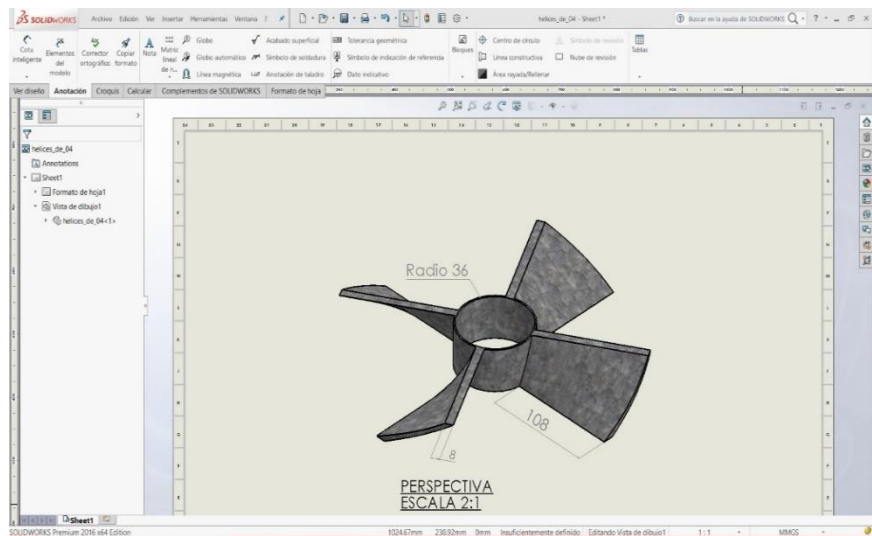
Dimensión de cuchilla cortadora del compostador
